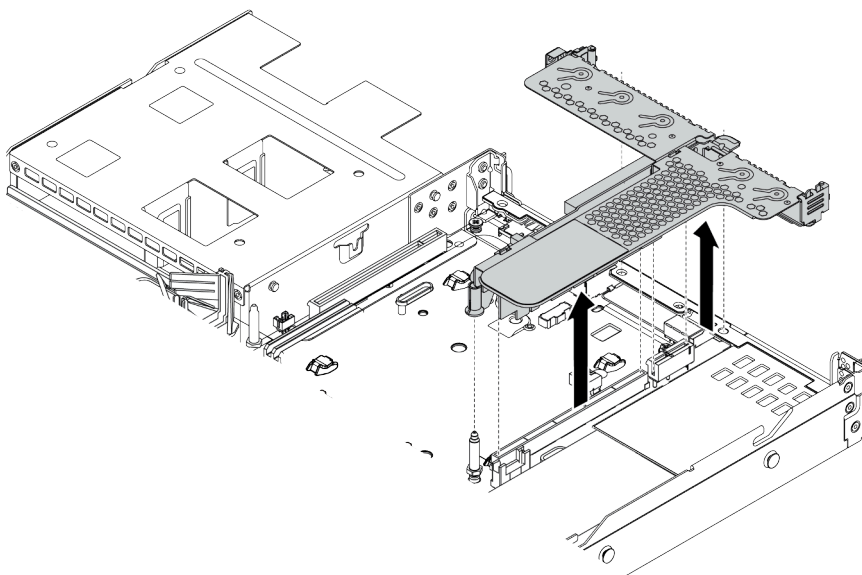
Entfernen der Adapterkartenbaugruppe
